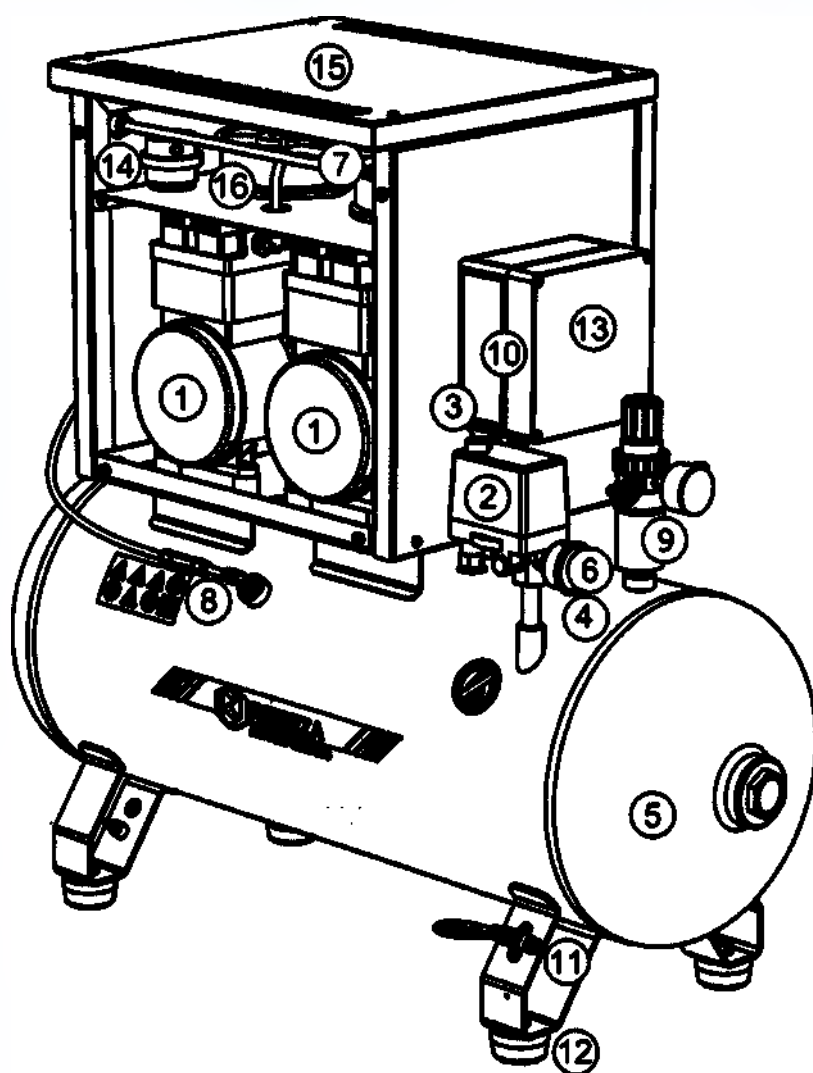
Общий вид компрессора KM-100.OLD15TK и KM-100.OLD20TK
